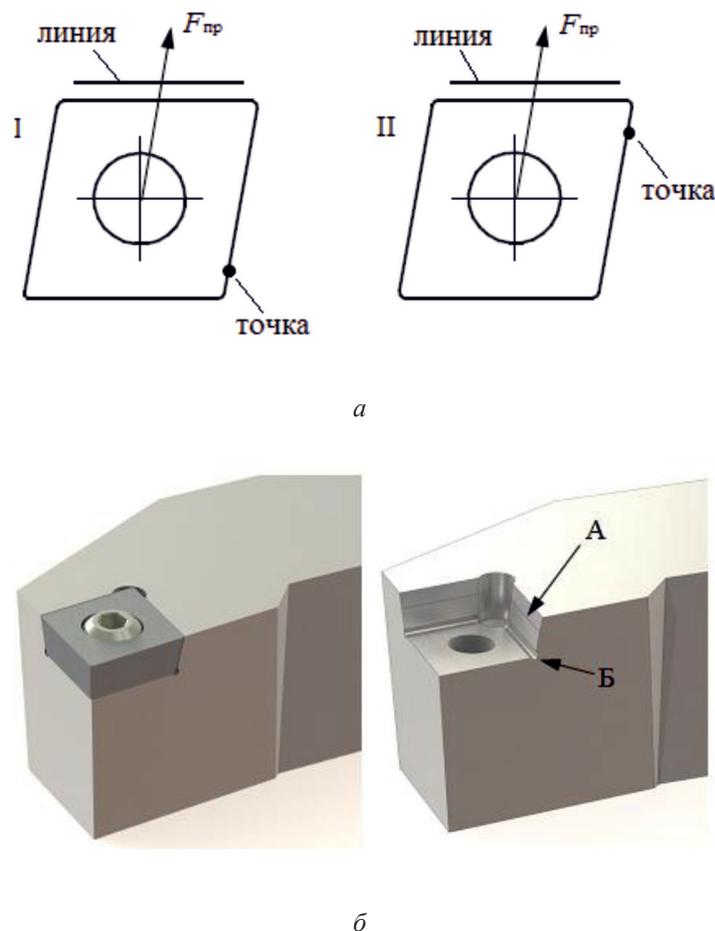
Схема базирования пластины в гнезде реза (а) и общий вид сборного режущего инструмента (б)
